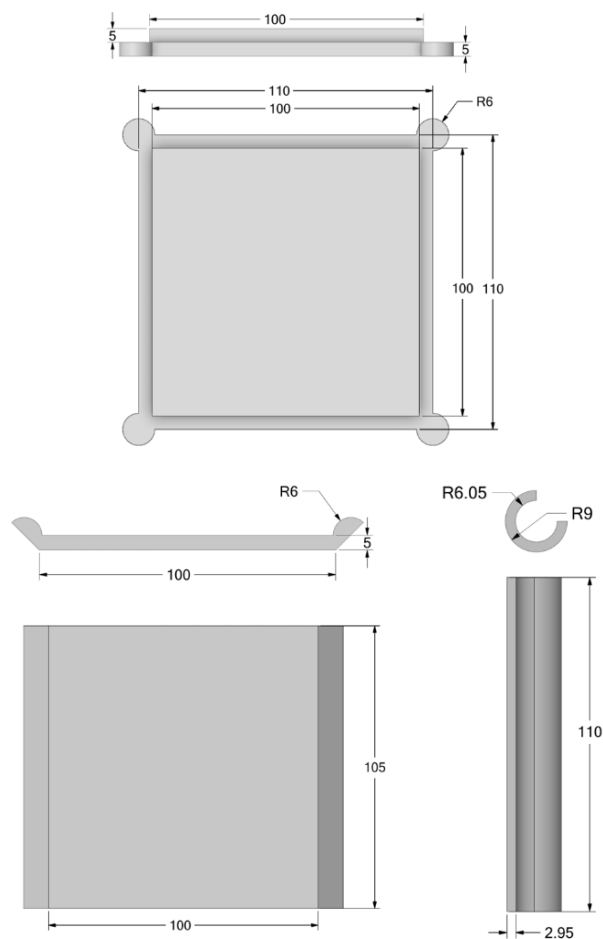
Профиль и основные размеры деталей разъемной формы
